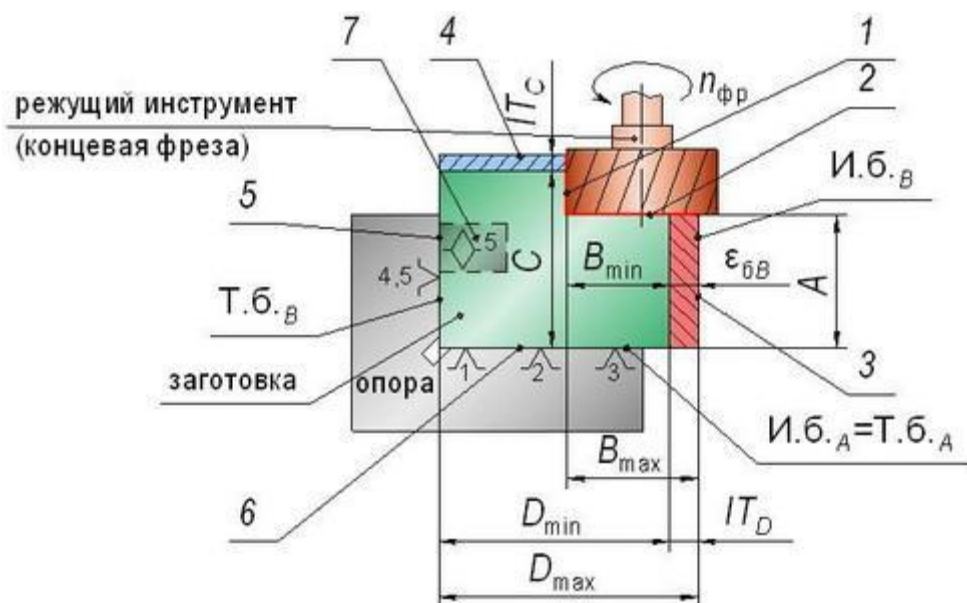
Фрезерование паза призматической детали: 1, 2 - обрабатываемые поверхности; A , B - размеры обработки; C , D - габаритные размеры заготовки; 3, 4 - свободные поверхности; 5, 6, 7 - базовые поверхности
